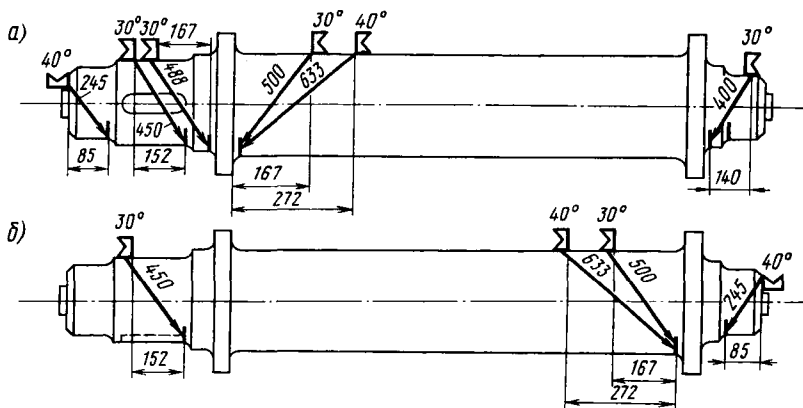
Схемы и зоны контроля наклонными искателями главного приводного вала эскалатора ЭТ-5М при различном расположении искателей (а, б)
